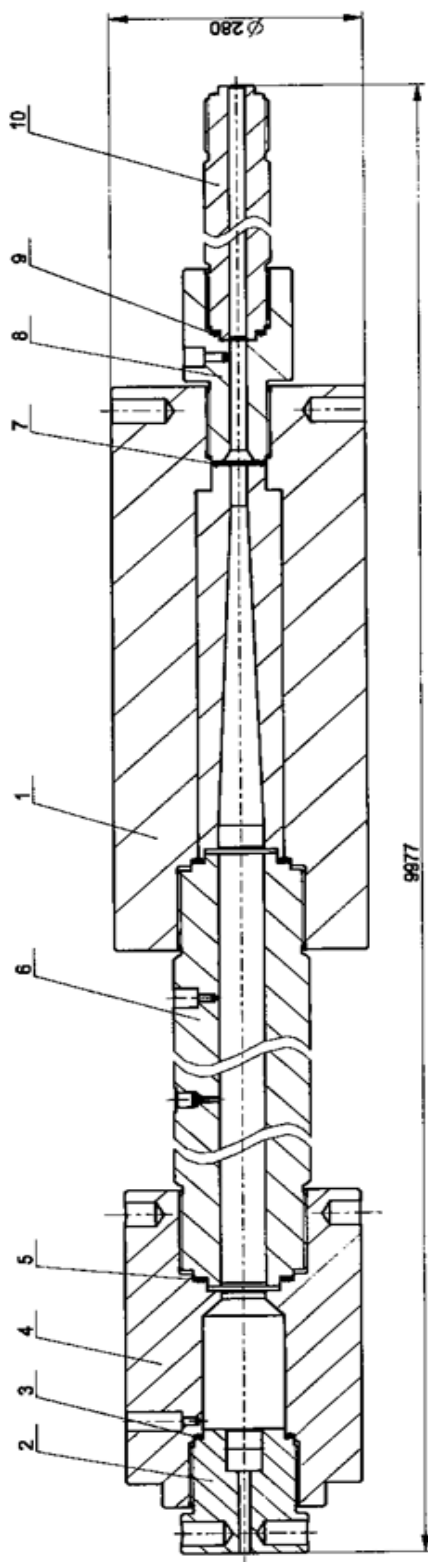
Сборочный чертеж двухступенчатой установки ГПМ (ППХ50/18).
